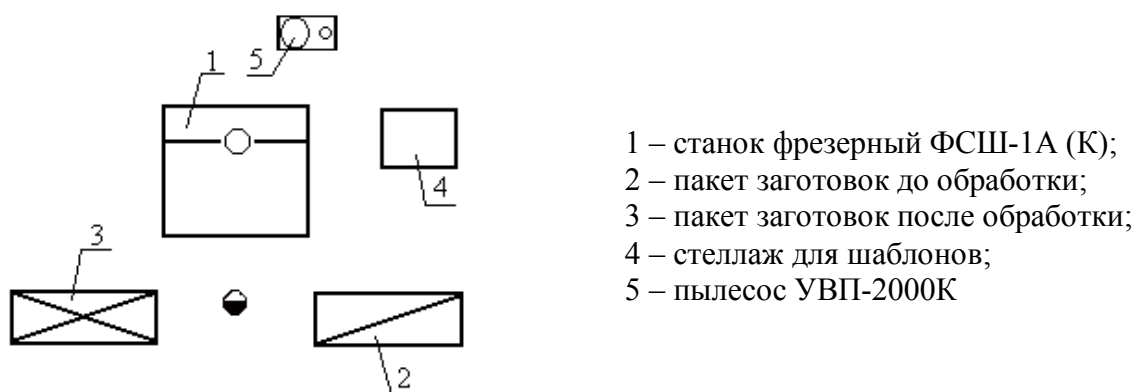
План рабочего места у фрезерного станка ФСШ-1А (К)
